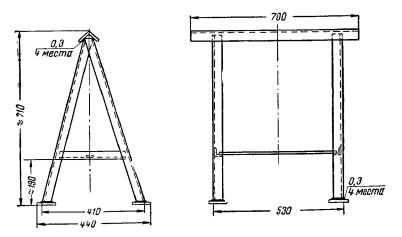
Козлы для разборки крышки трансформатора (размеры в мм).
